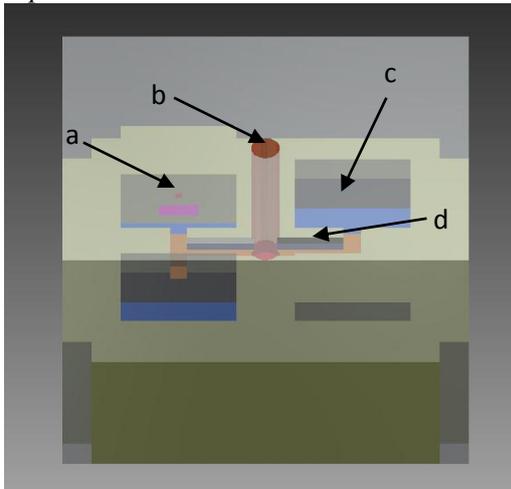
Komponen *micro mold bracket orthodontic* yang telah di assembly
